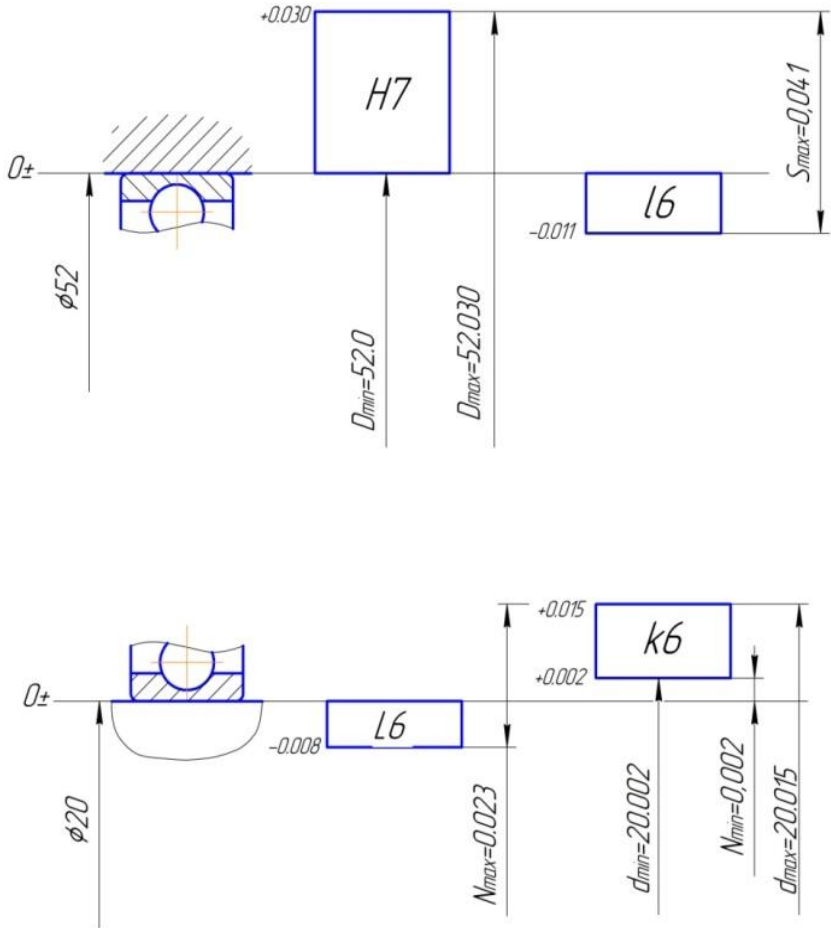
Схема розташування полів допусків підшипникового з'єднання
